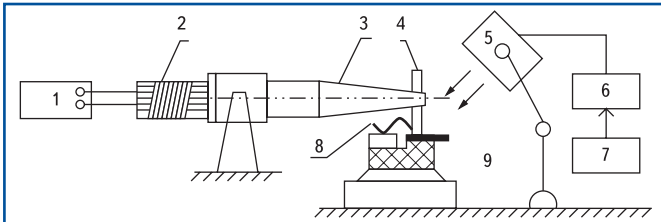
Схема УЗ-микросварки с ИК-активацией: 1 — генератор ультразвуковых колебаний; 2 — магнитострикционный преобразователь; 3 — ультразвуковой инструмент; 4 — сварочный капилляр; 5 — источник ИК-излучения; 6 — блок питания; 7 — блок управления; 8 — проволочный вывод; 9 — контактная площадка
